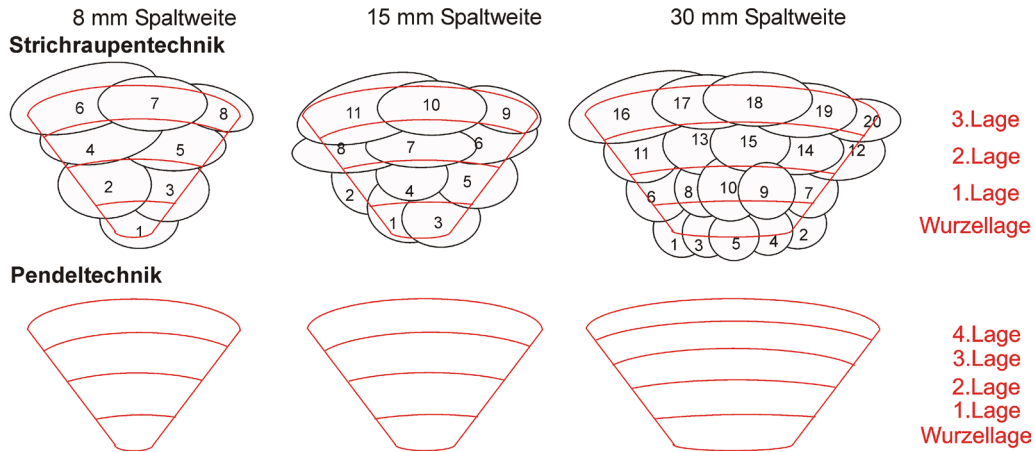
Nahtaufbau der beiden Schweißstechniken
